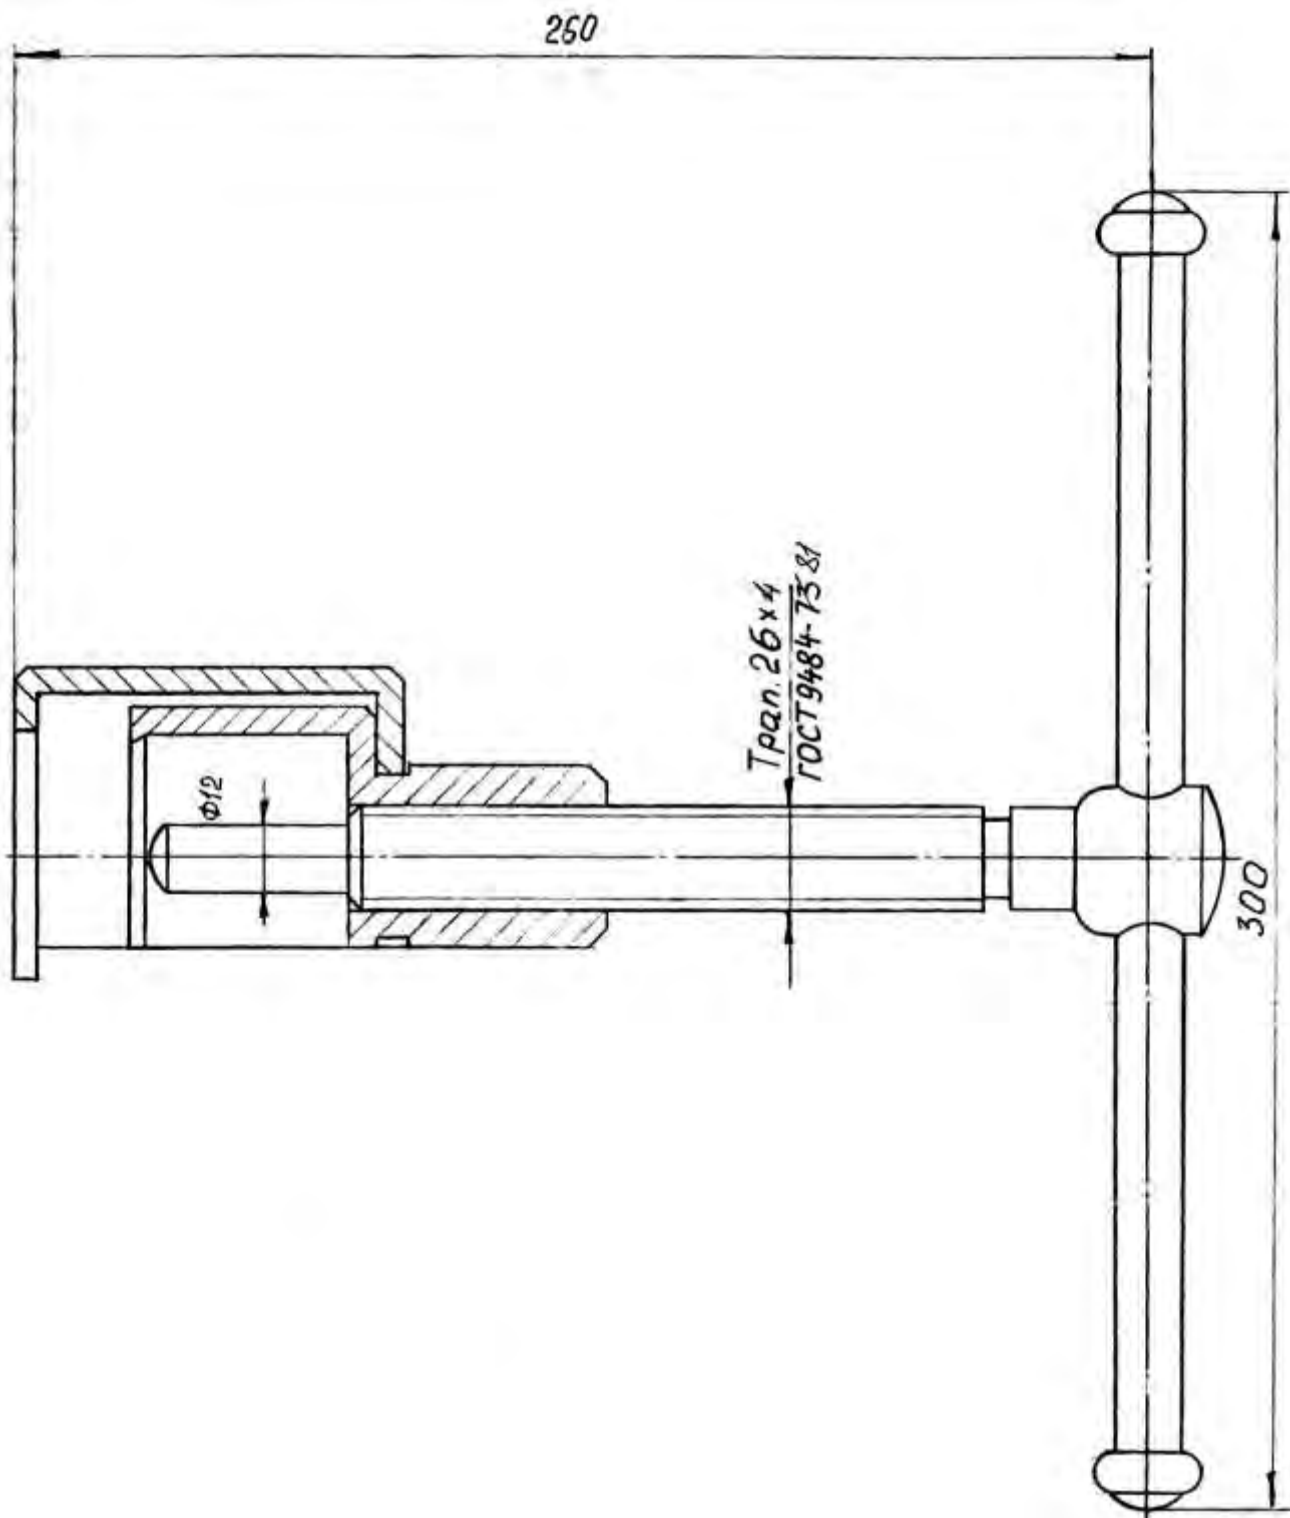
3М 7814-5118 Съемник втулки и звездочки коленчатого вала
